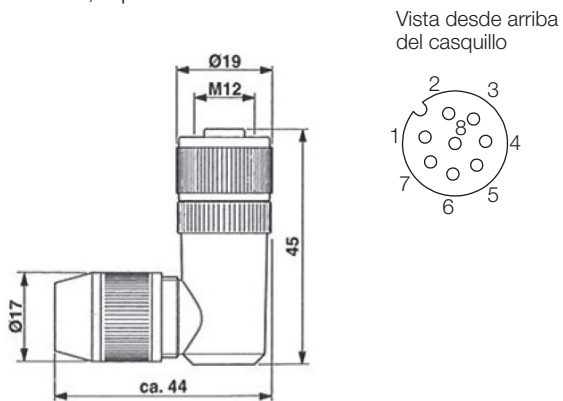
Conector BCC M488-0000-1A-000-43x834-000
